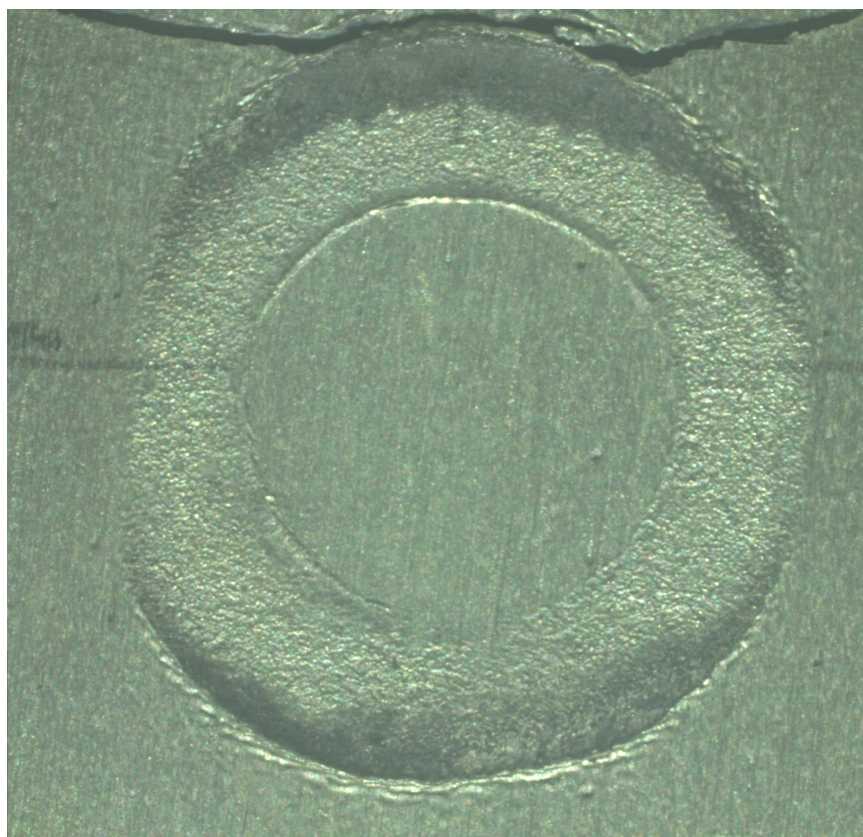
Характерный вид повреждения на поверхности полосы образца в зоне фреттинг- коррозии ($\times 6.5$, образец 1.1.2)
